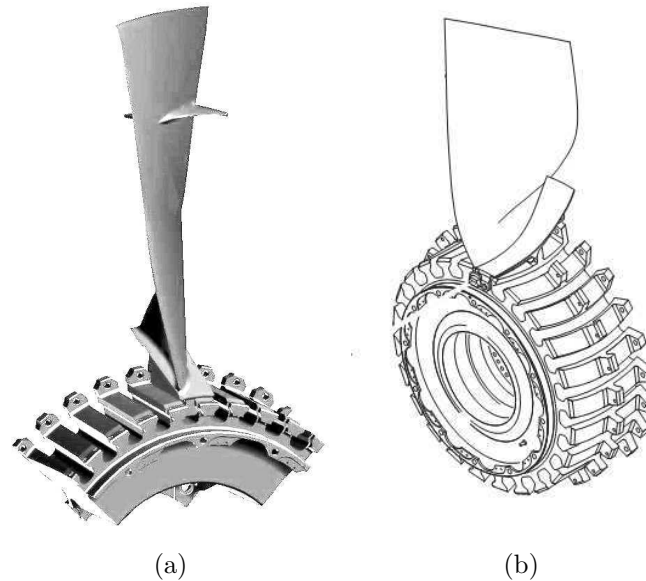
Vues du disque de la soufflante du CFM56-5 (a) et de la soufflante du CFM56-7 (b).
